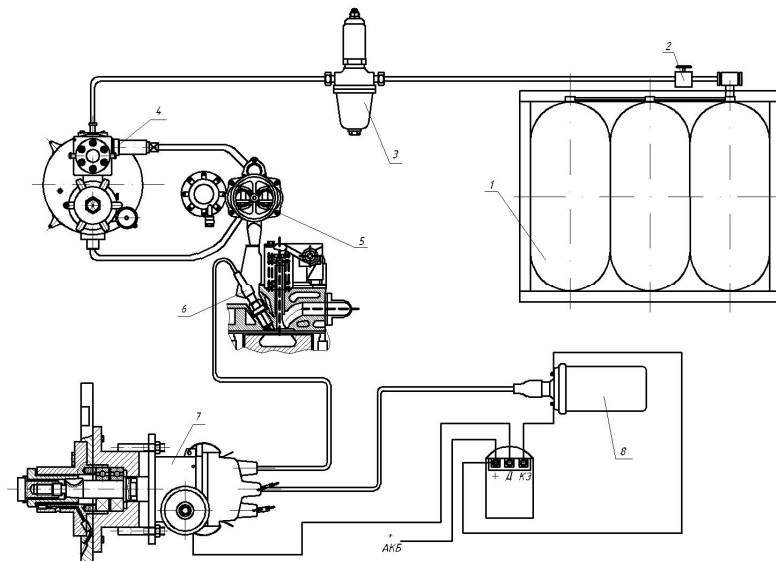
Схема систем живлення та запалювання газового двигуна: 1 – касета з газовими балонами; 2 – газовий вентиль; 3 – газовий клапан; 4 – двохступінчастий газовий редуктор; 5 – газовий змішувач; 6 – свічка запалювання; 7 – переривач-розподільник; 8 – привод переривача-розподільника; 9 – котушка запалювання.
